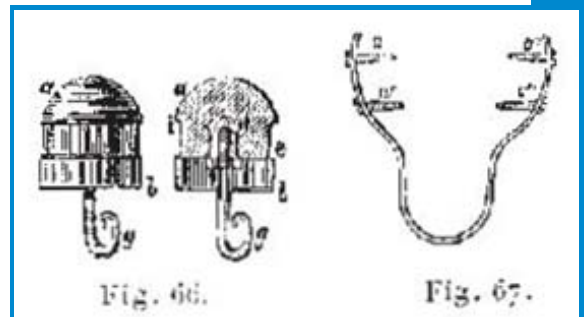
Fixation par bride. Croquis S. Saavedra.
